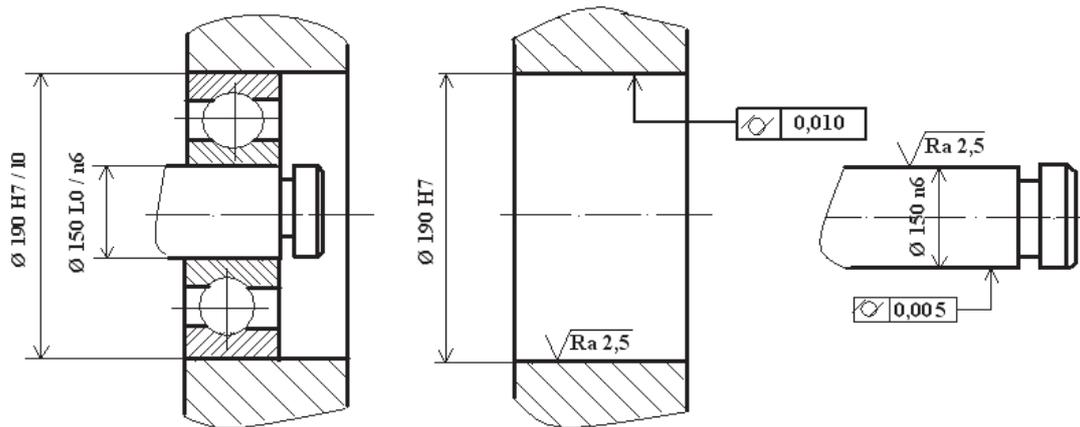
Эскиз подшипникового узла и детали подшипникового соединения
